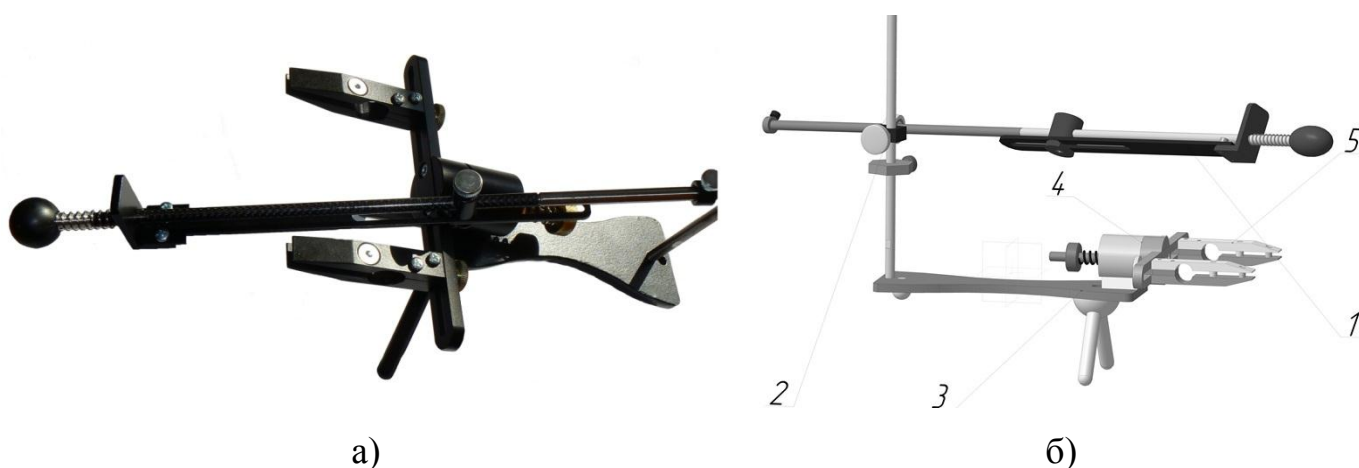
Пристрій для заточування леза ножа: а) загальний вигляд пристрою; б) модель, яка зображує основні механізми пристрою;
